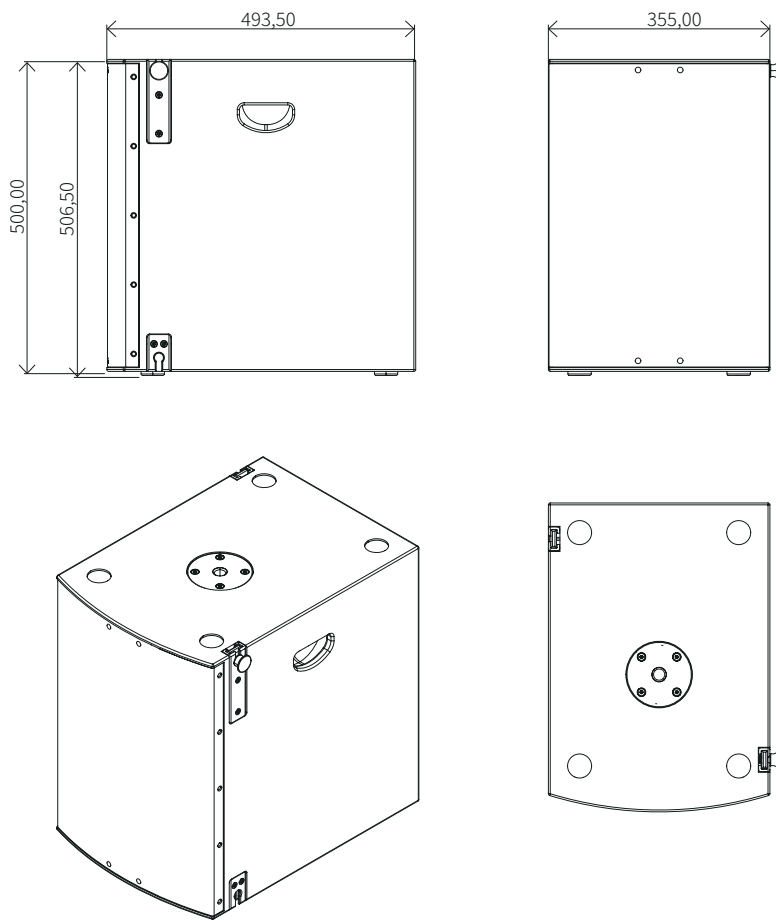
S12 PRO Ansichten und Abmessungen. Bemaßung in Millimetern.
